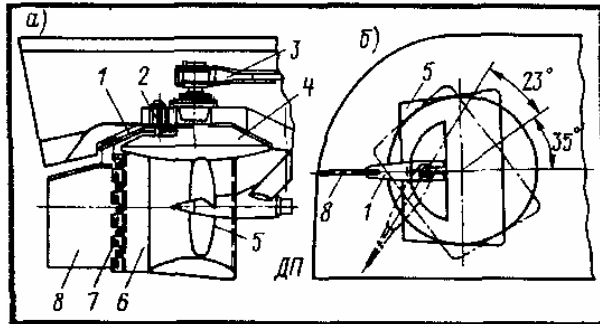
Схема поворотной насадки с подвижным стабилизатором: а - вид сбоку; б - вид сверху.
